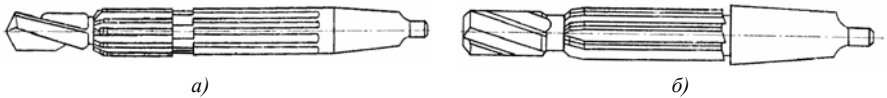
Різнотипні КОІ: а – свердло-розвертка; б – зенкер-розвертка
